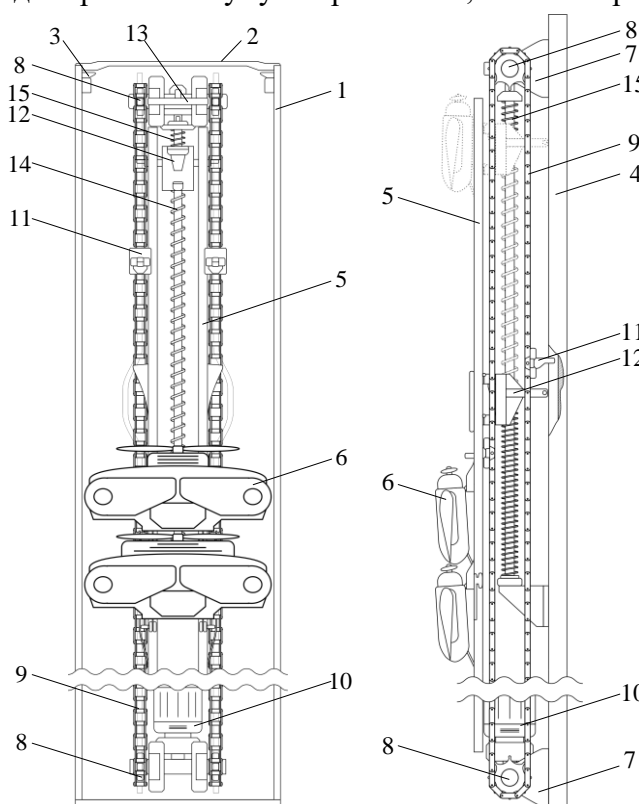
Устройство ТПК для множества БПЛА: 1 – корпус ТПК; 2 – разрушаемая крышка; 3 – пиропатроны; 4 – силовая балка; 5 – направляющие; 6 – БПЛА; 7 – опора; 8 – цепной блок; 9 – цепь; 10 – электродвигатель; 11 – зацепы; 12 – каретка; 13 – спусковой механизм; 14 – пружина силовая; 15 – пружинный амортизатор
